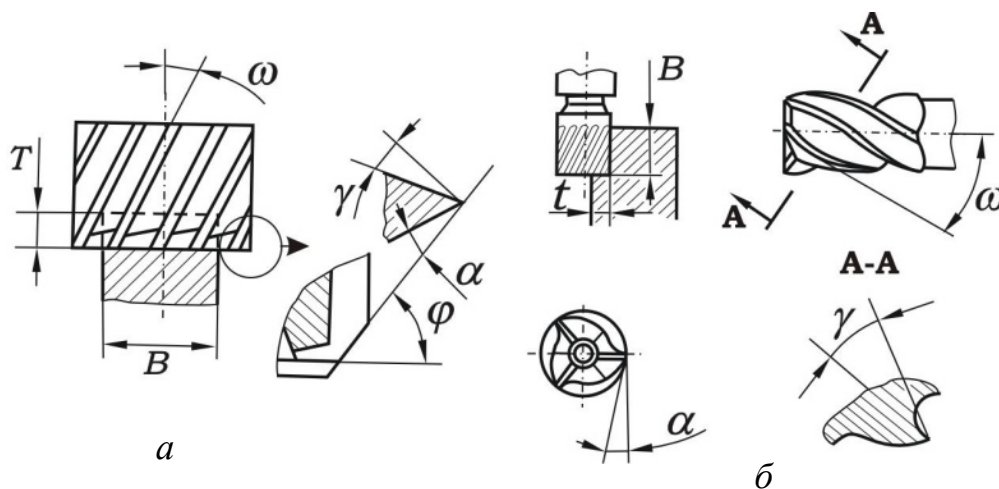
Схеми обробки й геометричні параметри робочої частини фрез:
